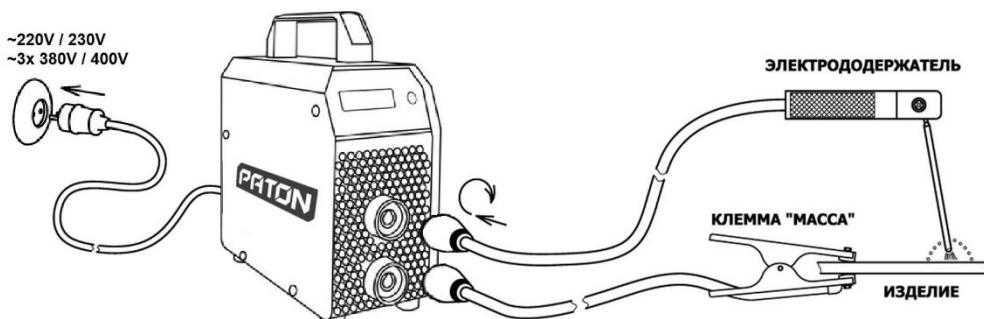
Схема подключения аппарата для сварки штучными электродами
